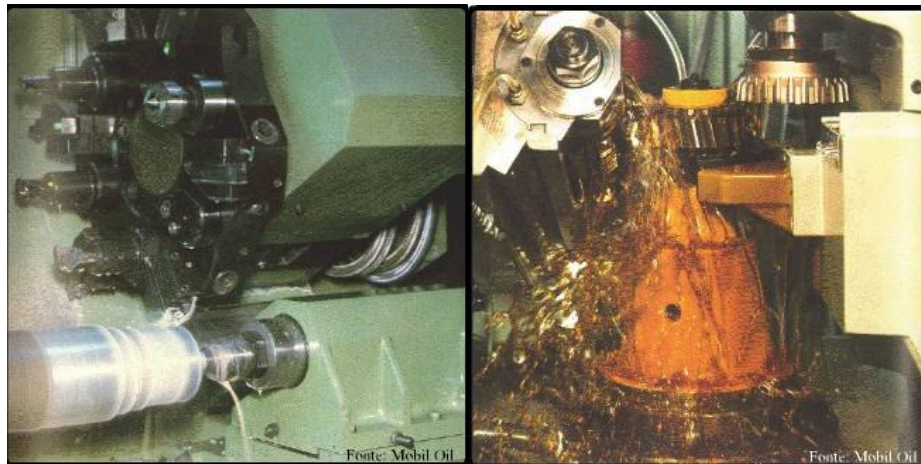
Emulsão utilizada em torneamento, óleo utilizado na fresagem de engrenagens.
